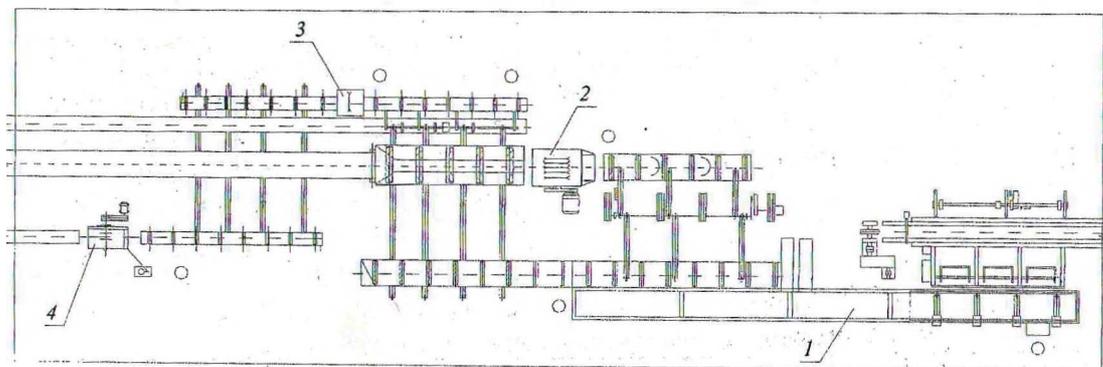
Технологическая схема лесопильного потока на базе вертикального ленточнопильного и круглопильного станков: 1 — вертикальный ленточнопильный станок ЛЛК-2; 2 — круглопильный станок для распиловки брусьев; 3 — торцовочный станок; 4 — фрезернообрезной станок
